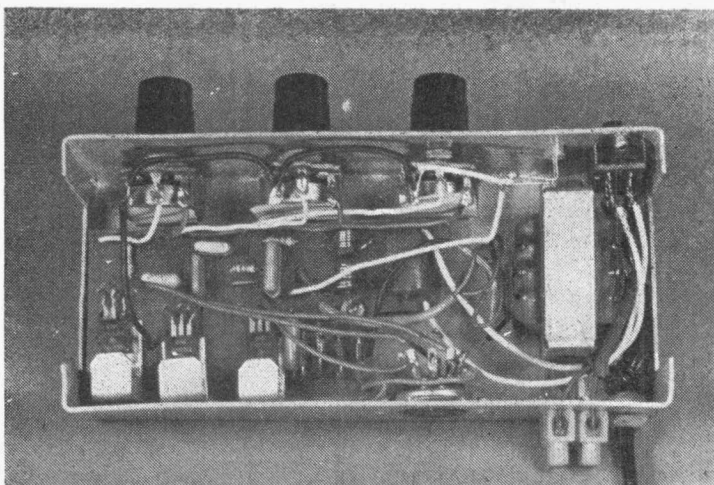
Vista da disposição da plaqueta e dos demais componentes dentro da caixa.
